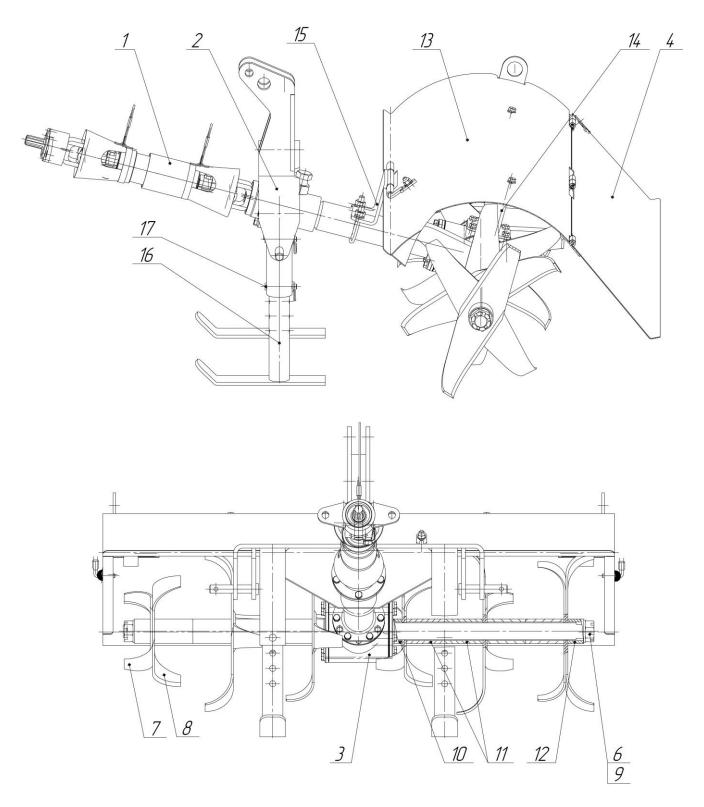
Фреза почвообрабатывающая ФР-00.700-Б 1 — карданный вал; 2 — кронштейн ; 3 — редуктор; 4 — створка; 6 - шплинт; 7 — лопасть правая; 8 — лопасть левая; 9 — гайка; 10, 11, 12— труба; 13 — кожух; 14 — стойка; 15 — опора; 16 — лыжа; 17 - палец
